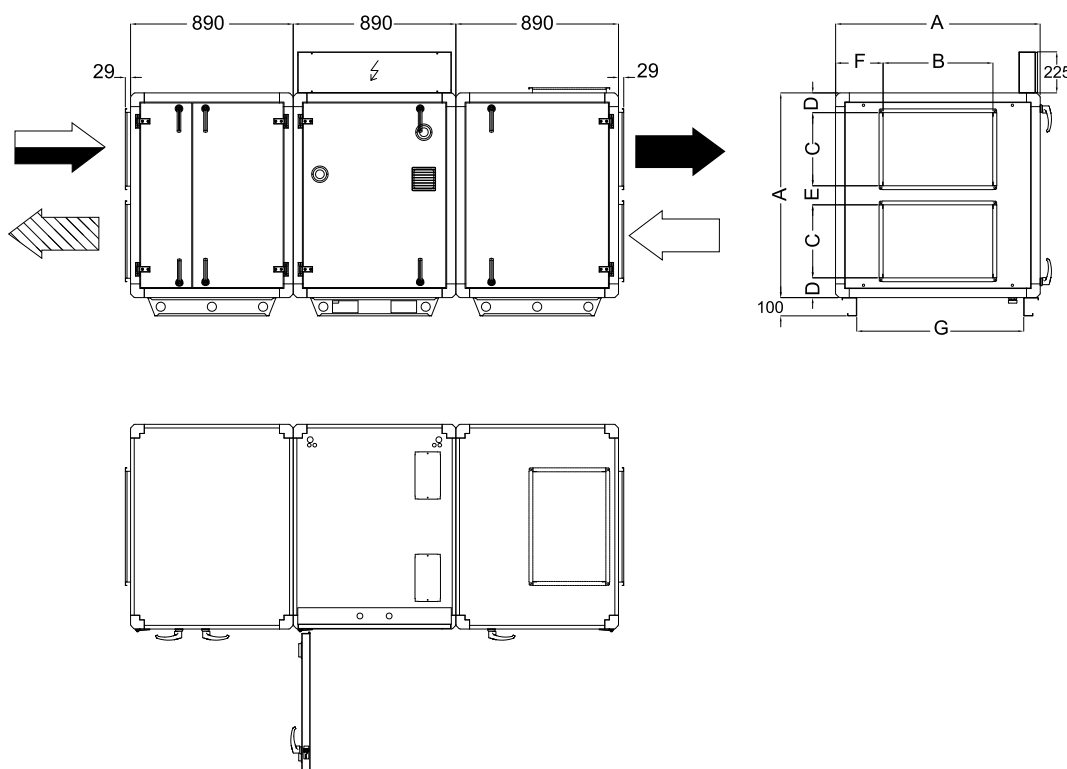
Abmessungen (mm) SR09, SR11 (als linksseitiges Gerät gezeichnet)
